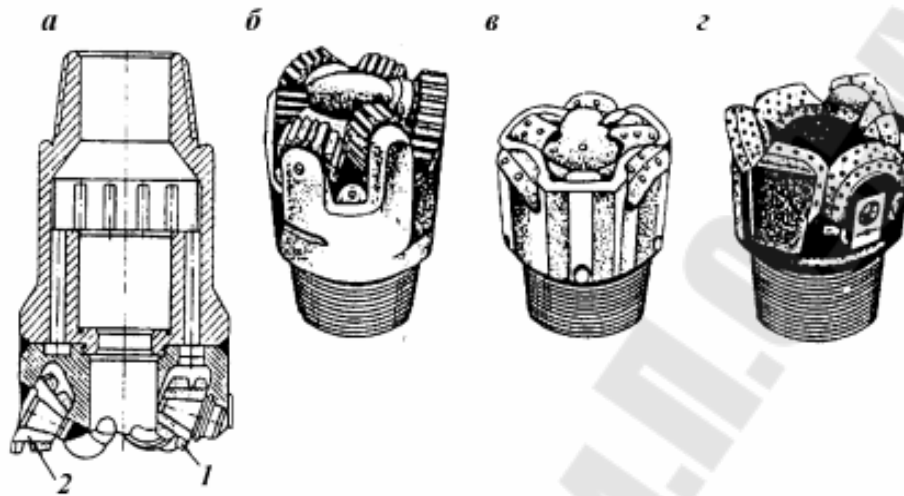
Шестишарошечные бурильные головки с литым цилиндрическим корпусом: а – с шарошками в форме усеченных конусов, имеющих фрезерованное вооружение; б – с шарошками в форме цилиндров, имеющих фрезерованное вооружение; в – с шарошками двухконусной формы, имеющими твердосплавное, карбидвольфрамовое вооружение (зубки); 1 – внутренняя кернообразующая шарошка; 2 – наружная скважинообразующая шарошка
